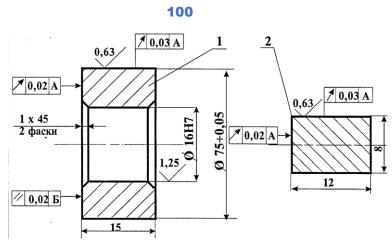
Рабочий чертёж стального диска и образца: 1-диск, 2-образец.
